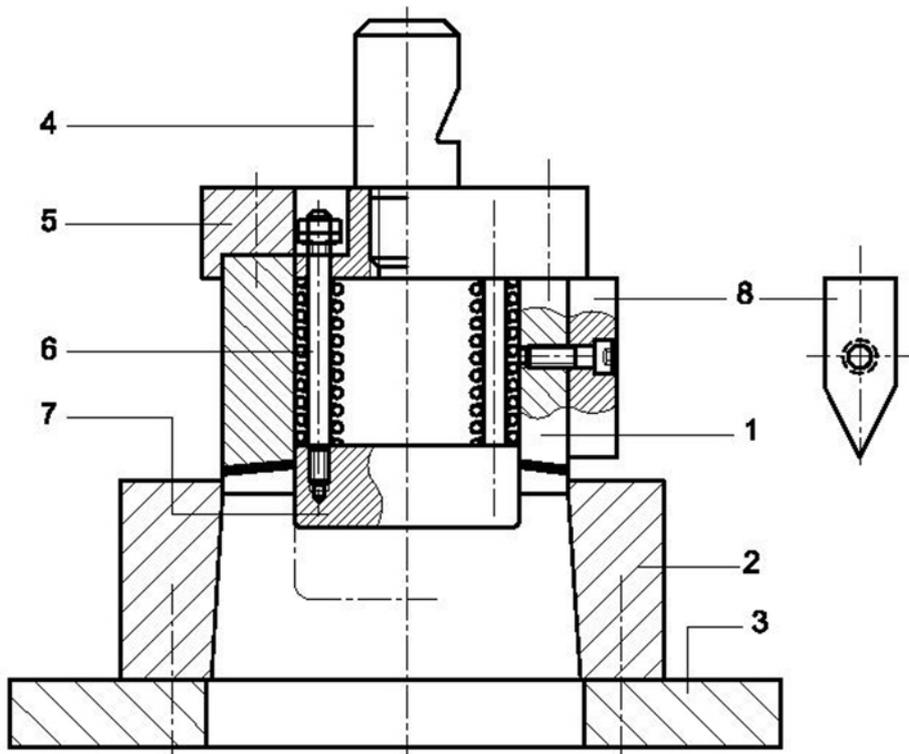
Feinstanzwerkzeug Ringzacke
